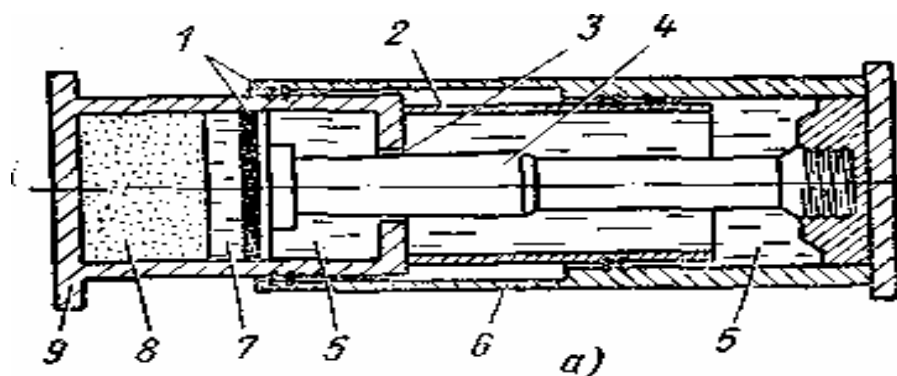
Бампер с гидропневматическим амортизирующим элементом: 1 — уплотнение; 2 — гильза; 3 — дросселирующее отверстие; 4 — шток; 5 — полость корпуса бампера; 6 — цилиндр; 7 — поршень; 8 — полость; 9 — корпус бампера
